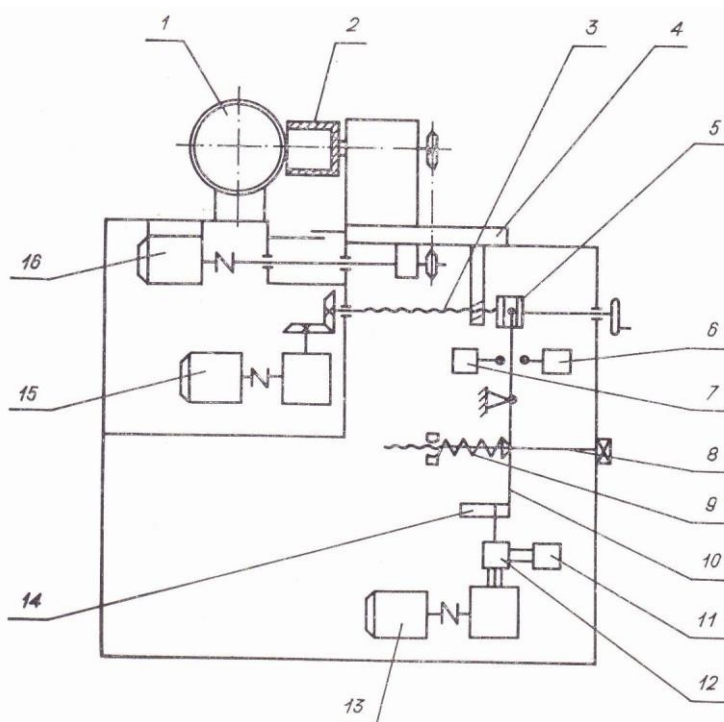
Кинематическая схема экспериментального стенда: 1 – круг; 2 – заготовка; 3 – ходовой винт; 4 – стол; 5 – обойма; 6, 7 – концевые выключатели; 8, 9 – механизм регулирования усилия подачи; 10 – рычаг; 11 – электромагнит; 12 – муфта; 13 – привод прерывистой подачи; 14 – кулачок; 15 – привод подачи стола; 16 – привод вращения заготовки
